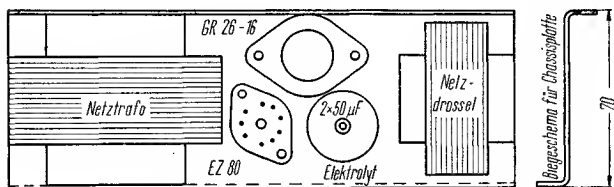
Aufbauschema für das Chassis des Universal-Netzgerätes
